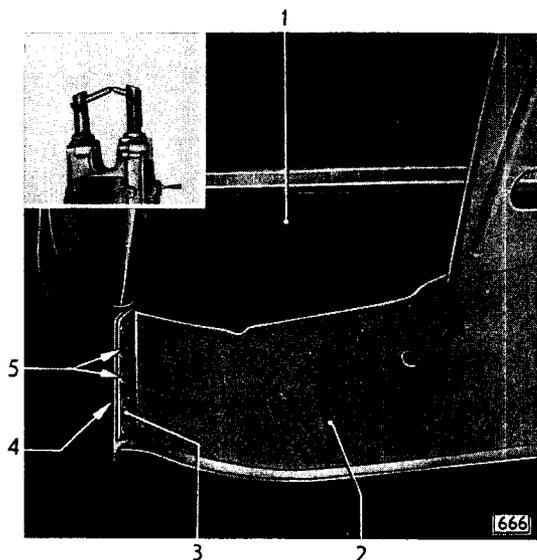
Senkrechter Flansch der rechten Seitenstrebe punktgeschweißt – Linke Seitenstrebe in gleicher Weise punktschweißen
